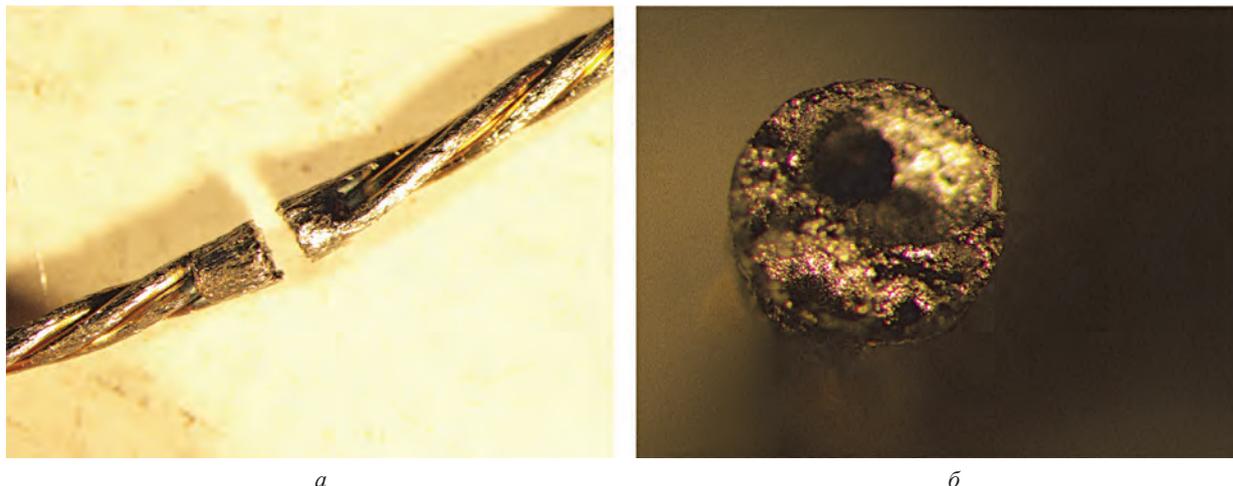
Внешний вид разрушения (обрыва) сварки металлокорда (а) из-за наличия внутренней поры в зоне сварного шва (б)
